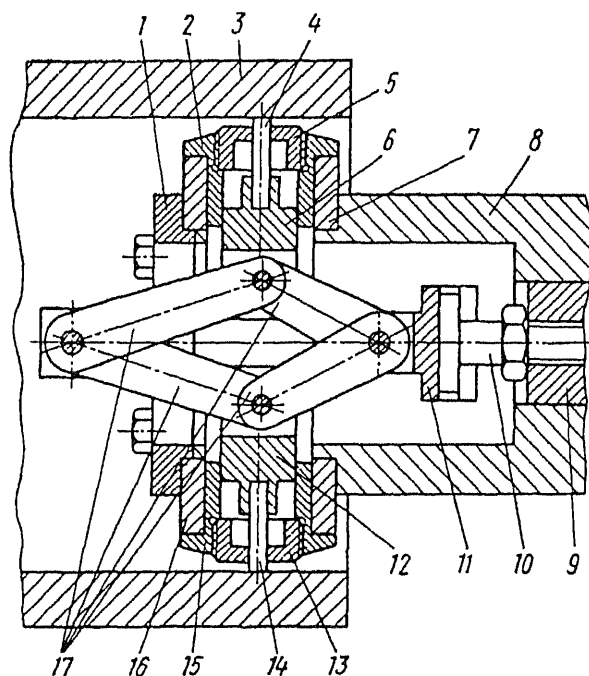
Приспособление для ФАБО цилиндров двигателя
